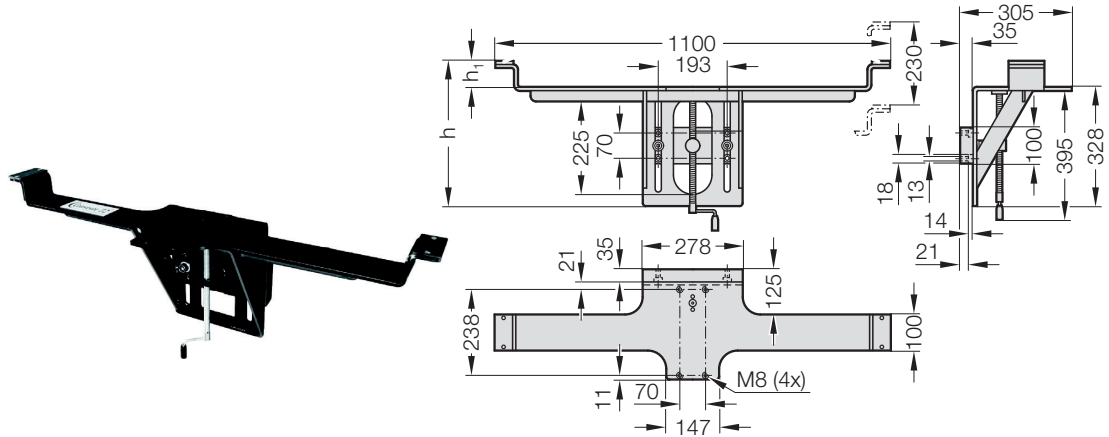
Angle de montage réglable en hauteur pour montage de barre profilée
